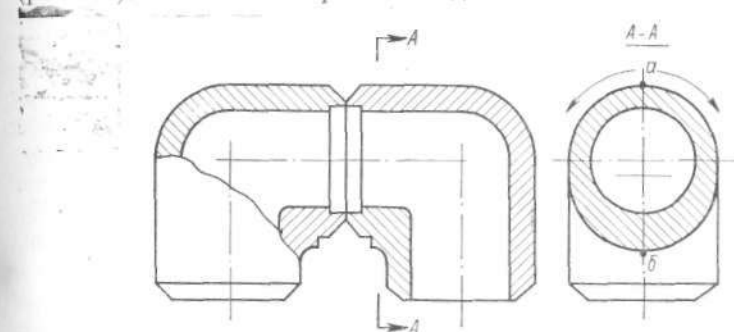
Сварное соединение с переменным сечением кромок.
